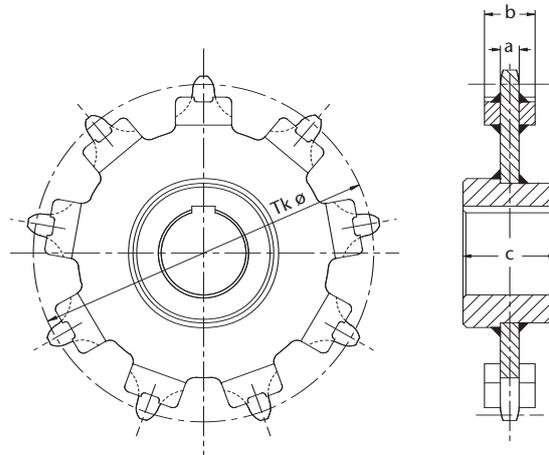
HEKO Kettenrad Typ GIE, innenverzahntes, einteiliges Kettenrad mit angeschweißter Kettenauflage
